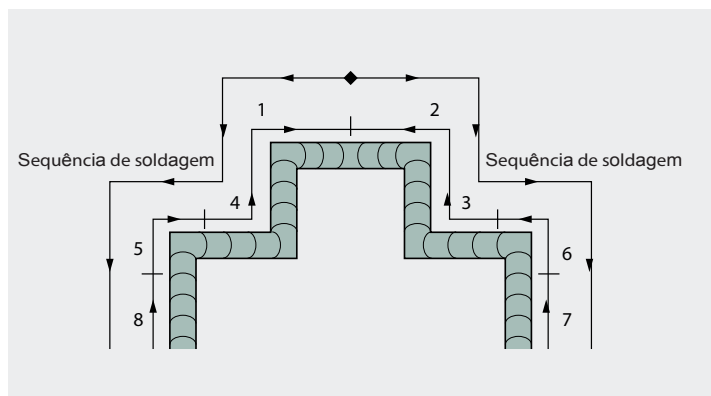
Exemplo de técnica de soldagem em passe a ré
